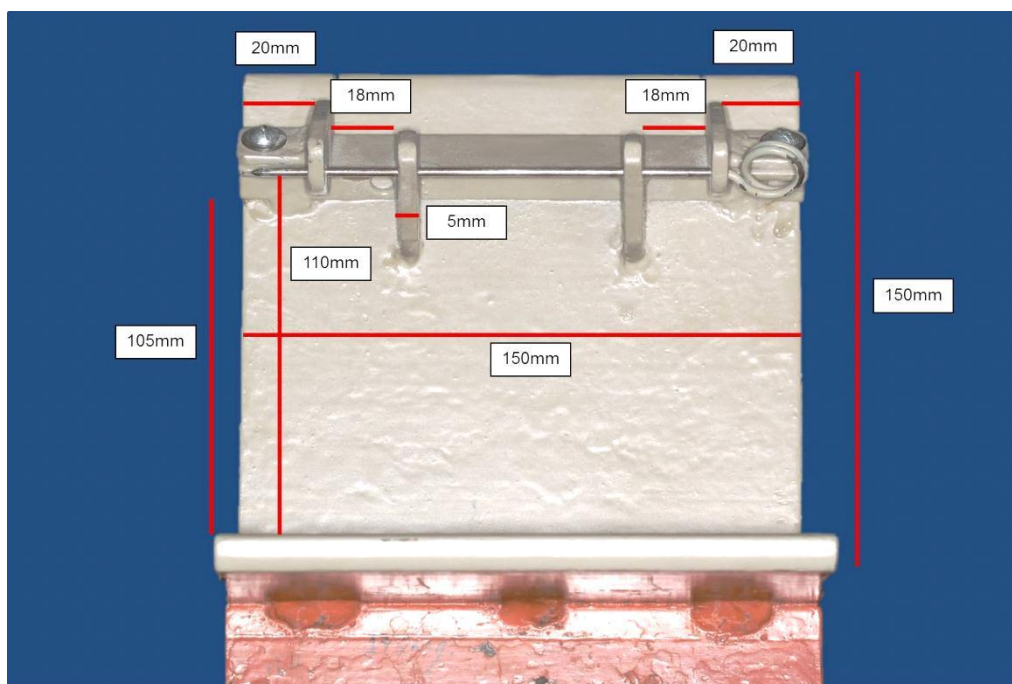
Vista frontal do suporte para testes, demonstrando todas as dimensões.
